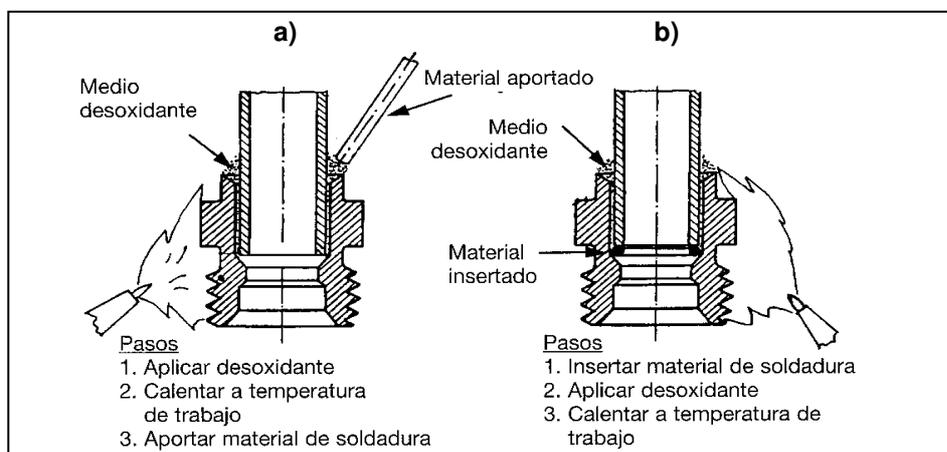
a) Soldadura con aportación de material; b) Soldadura con material insertado
